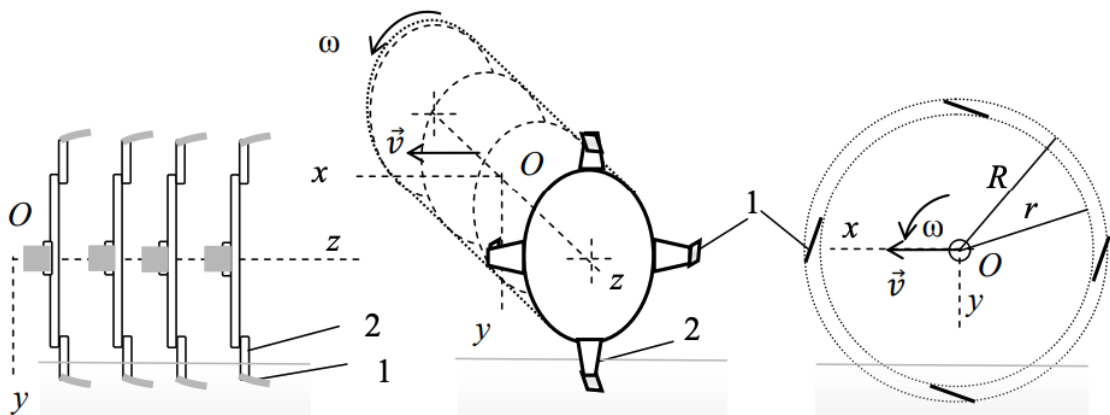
Барабан фрезы с ножами 1 и боковинами с режущими кромками 2
